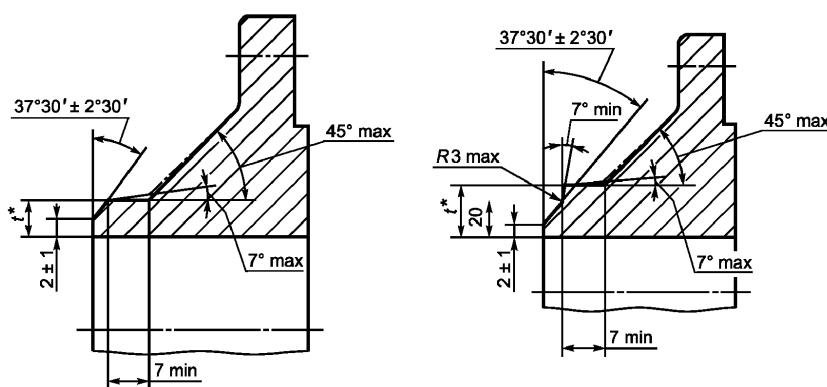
Разделка кромки под сварку для фланцев типа 11, ряд 2
